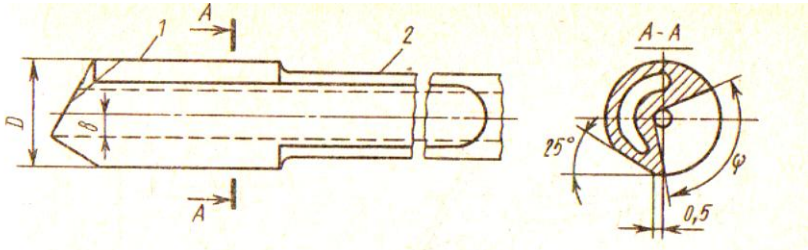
а. Ружейное сверло: $D=8-30\text{мм}$, состоит из рабочей части 1 и трубчатого корпуса 2
